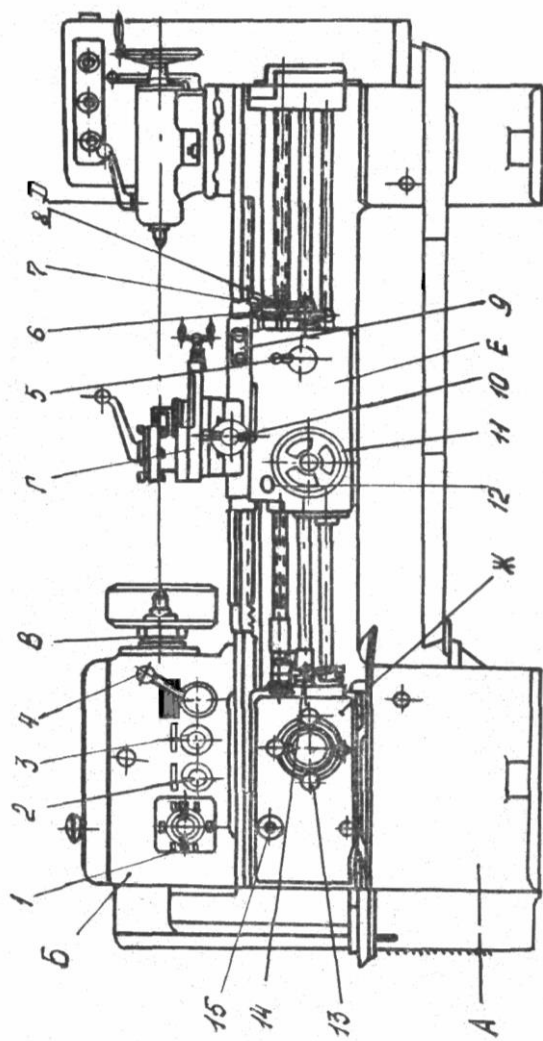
Общий вид основной части и органы управления станка 1К62:
